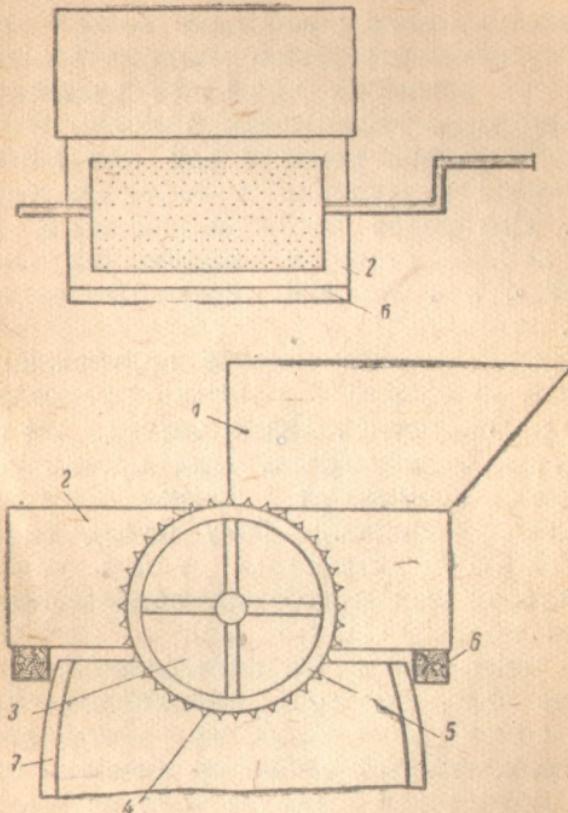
Ручная картофельная тёрка с барабаном: 1 — ковш для засыпки картофеля, 2 — ящик, 3 — тёрочный барабан, 4 — железный лист со множеством отверстий, 5 — деревянный обод, на который набит железный лист (тёрочный барабан), 6 — брускок, 7 — стенки бочки, на которые поставлена тёрка.
